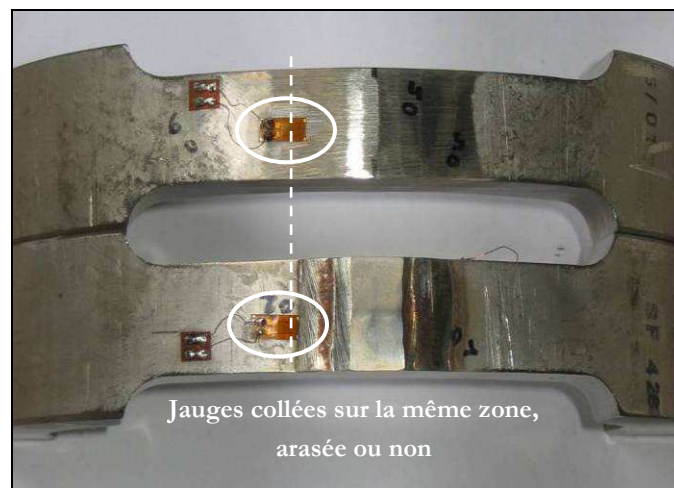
emplacement des jauges sur maquettes soudées-arasées (haut) et soudées (bas)
